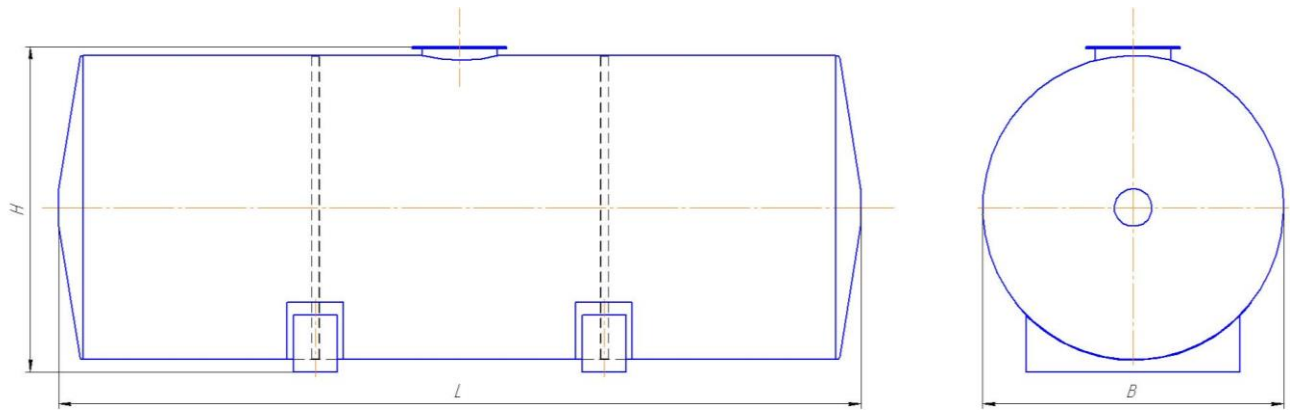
Горизонтальный резервуар, однокамерный с коническими днищами.
